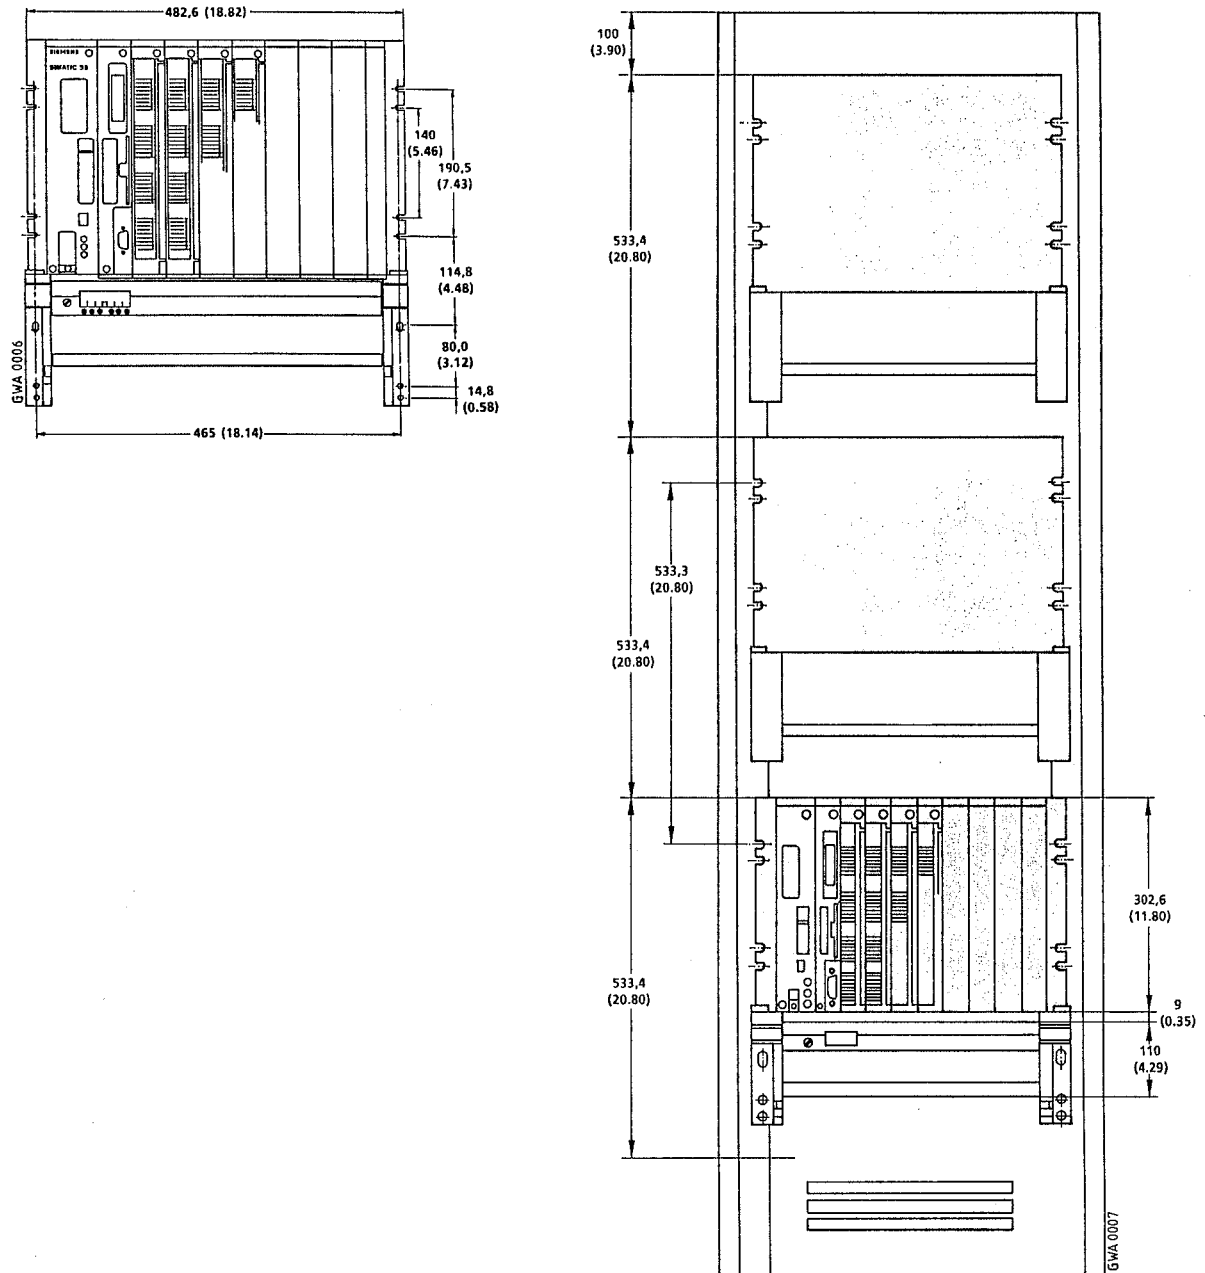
Bemaßung beim Einbau in 19"-Schränke
